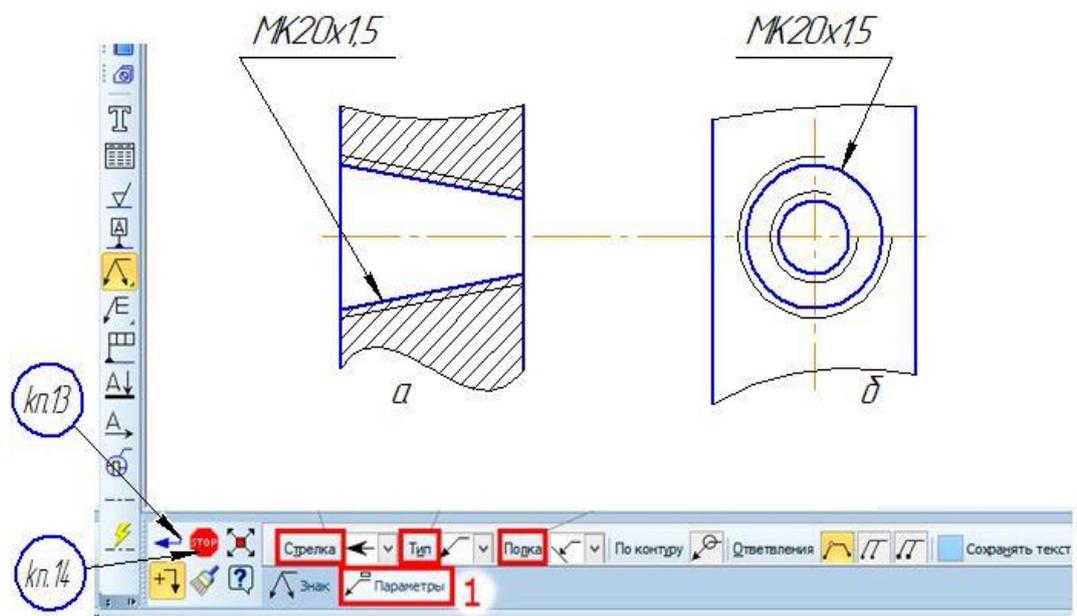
Обозначения внутренней метрической конической резьбы
